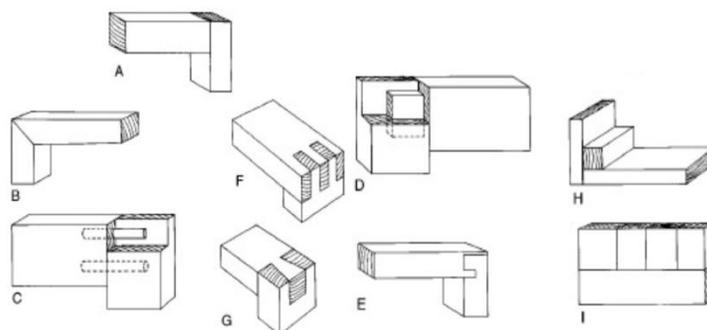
Uniones carpinteras (madera-madera): A, plana; B, biseccional; C, tarugada; D, cajuela y espiga; E, ensambladura de lengüeta y ribete; F, dentada; G, cola de milano; H, reforzada; I, Ranura y espiga.
